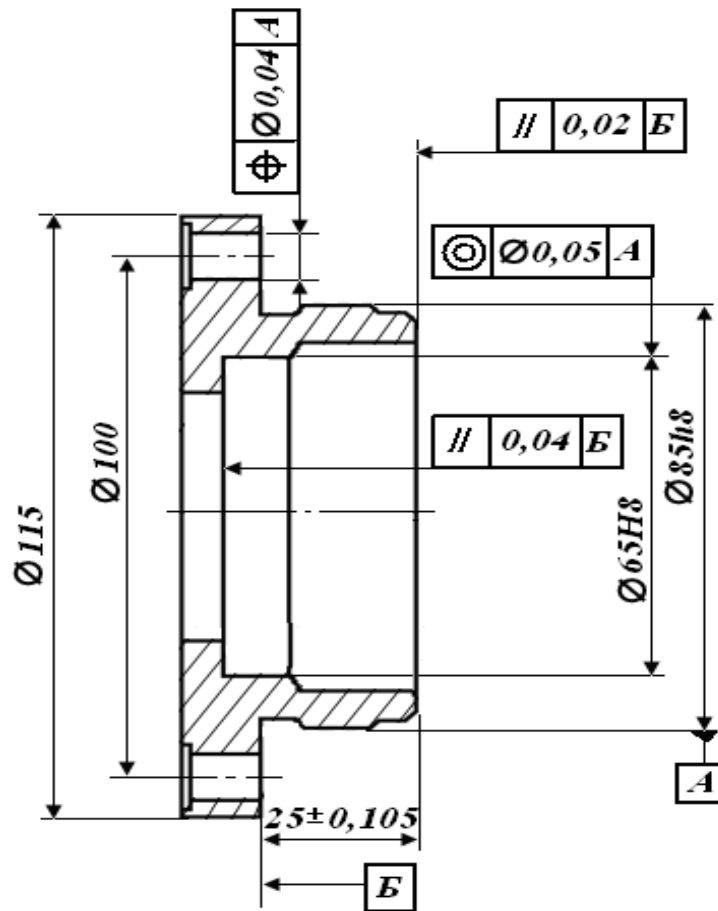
Ескіз кришки з зазначенням баз, допусків форми і розташування поверхонь
